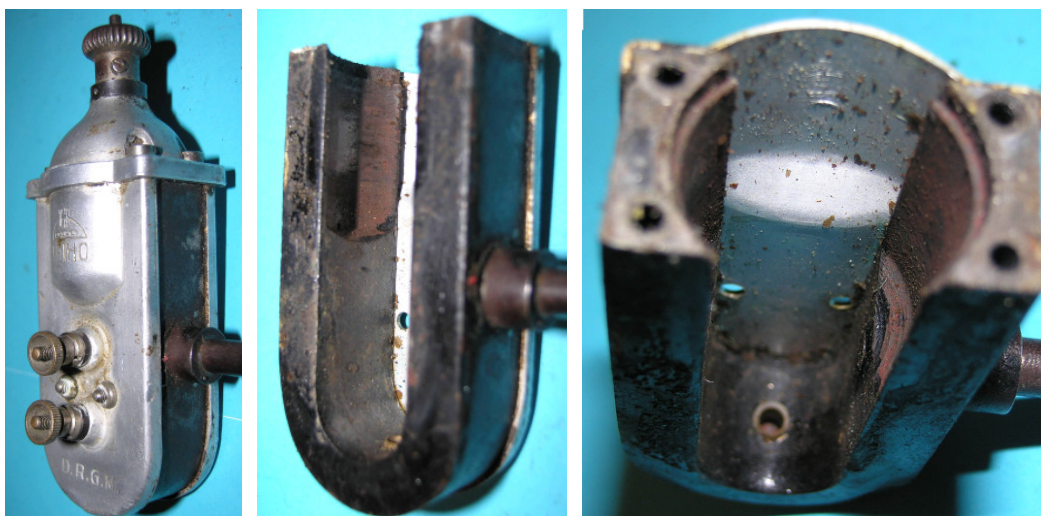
Gefräste Kontur des Polbogens im Hufeisenmagneten
